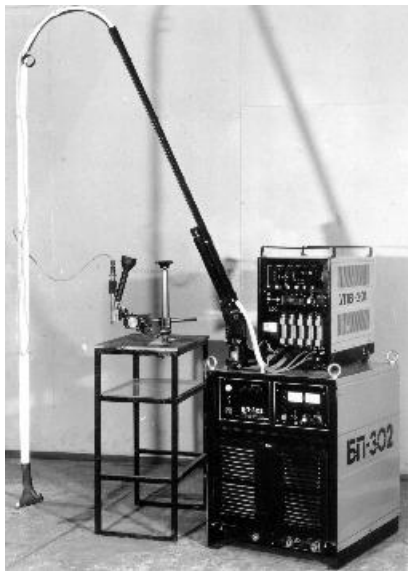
Установка для скоростной плазменной наплавки УПВ-301
